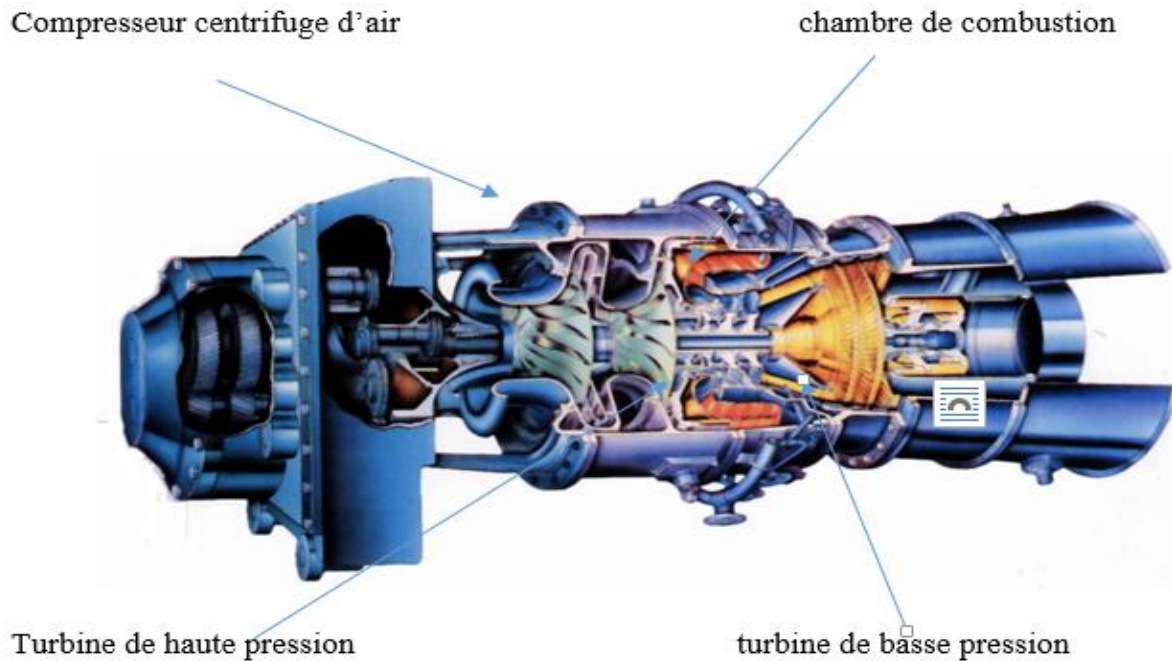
Vue d'ensemble de turbine à gaz DR 990.
